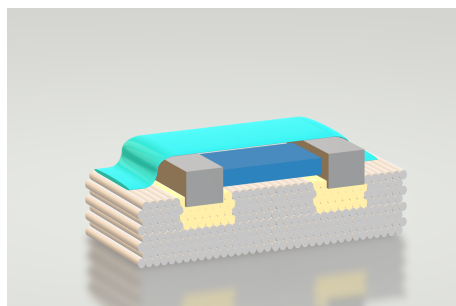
Kontaktování termokompresí - Posazení fóliového pouzdra
